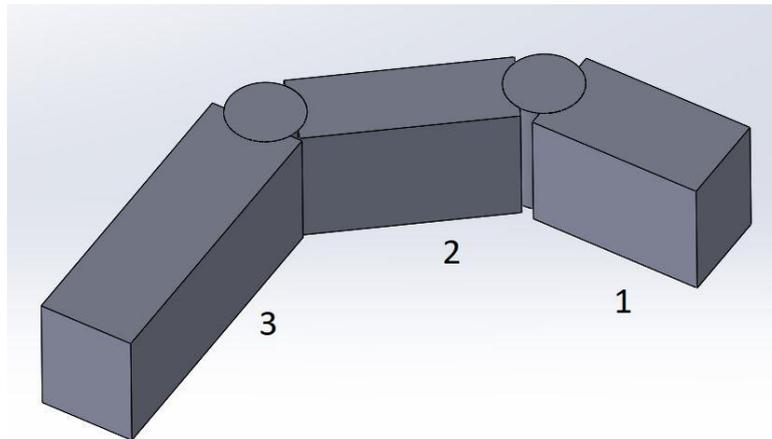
Detalle de pieza de anclaje en posición de amarre del vehículo
